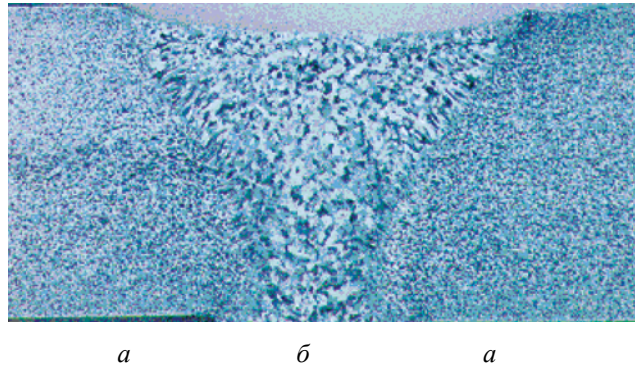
Структура узла сварки сплава АМг5 [2]:
